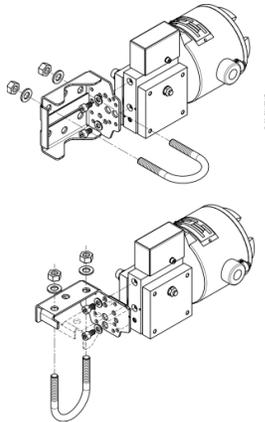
DW10-DA10- Befestigung der Halterungen für 2"-Rohr
